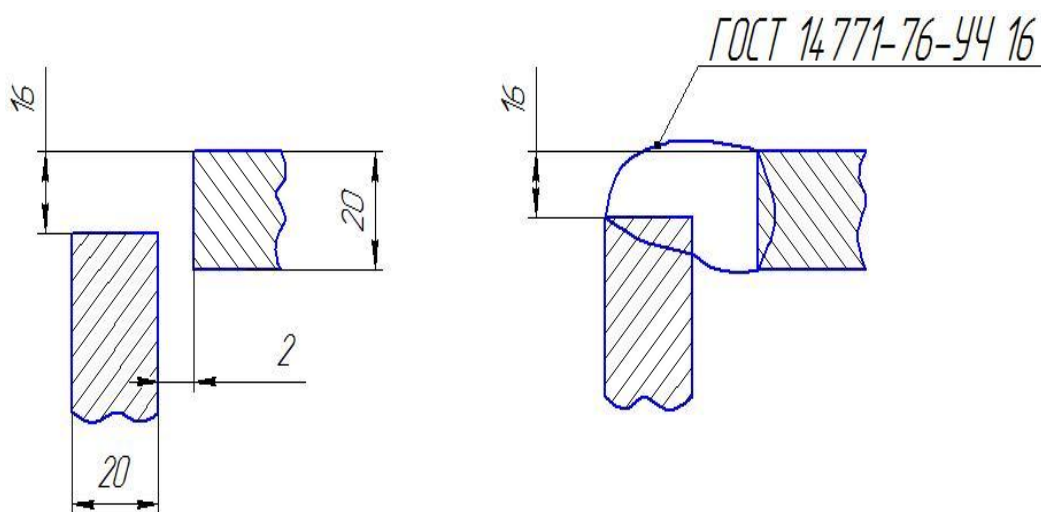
Подготовка кромок и вид сварного шва
